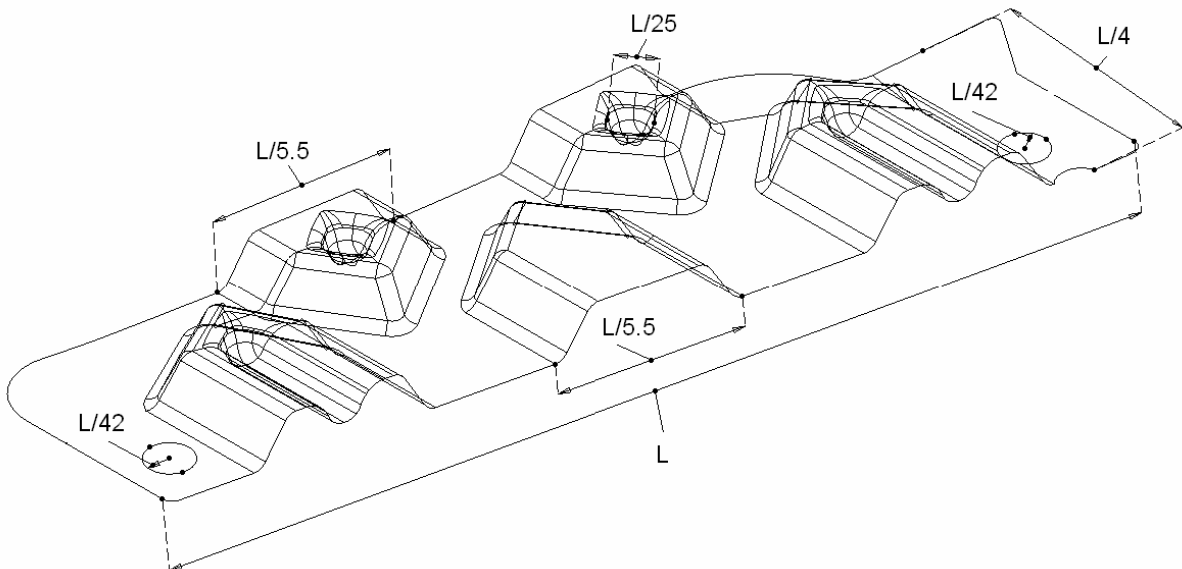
Forme de la pièce et données dimensionnelles en vue isométrique.
